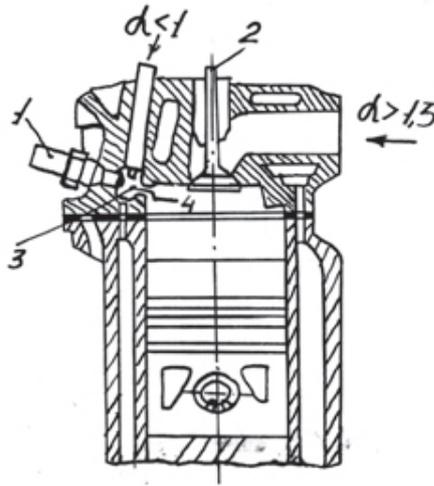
Схема двигателя с форкамерно-факельным процессом: 1 – свеча зажигания; 2 – впускной клапан; 3 – форкамера; 4 – впускной канал форкамеры
